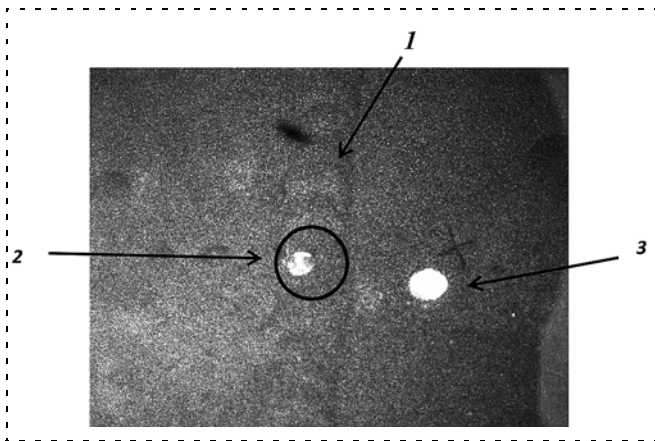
Изображение сварного шва на стальной пластине: 1 — сварной шов; 2 — метка для высверливания; 3 — отверстие от предыдущих измерений (не рассматривается)
